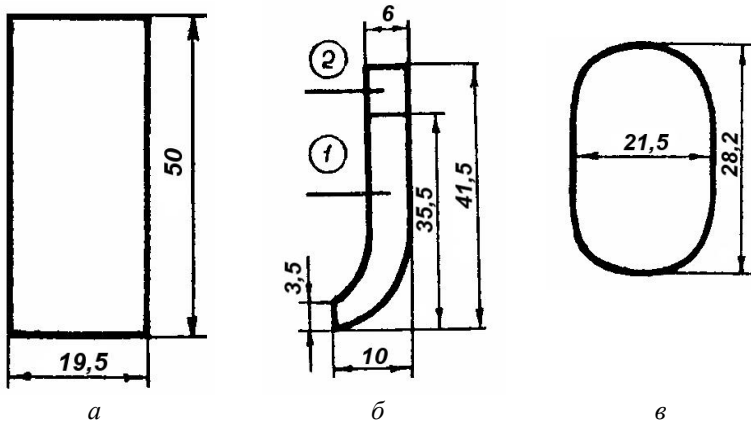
Схема побудови лекала: а – підкладки задньої кишені; б – підкладки і прокладки до відкоска; в - підкладка леї
